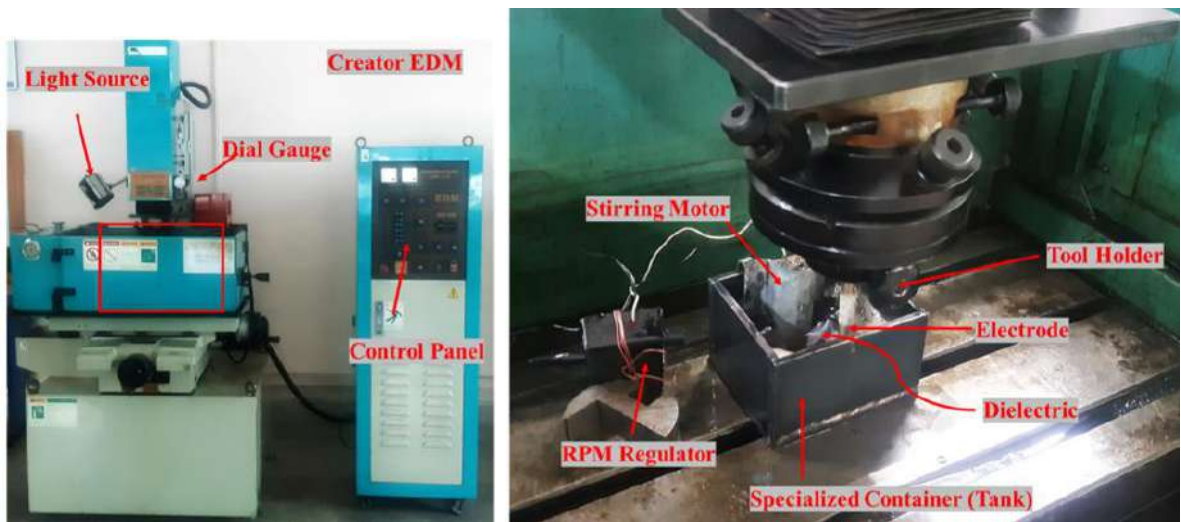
Робоча установка електроерозійної обробки [26]
